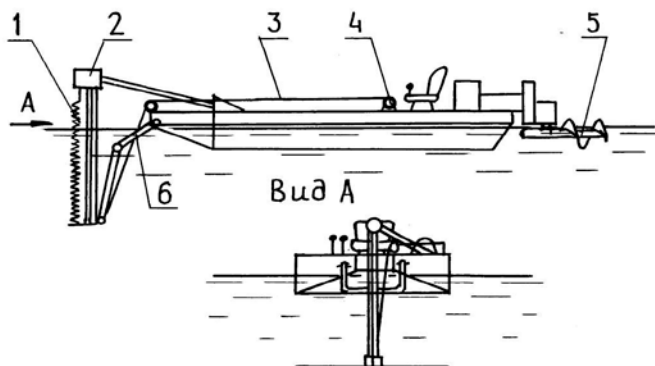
Схема косилки с Т-образным рабочим органом: 1 – Т-образный рабочий орган; 2 – редуктор; 3 – канат; 4 – лебедка; 5 – шнековый винт; 6 – двухзвенная стрела
